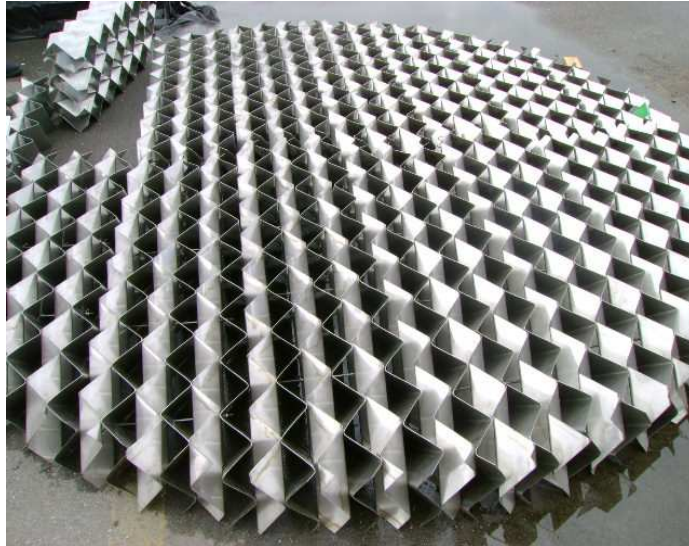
Paquete o elemento de empaque estructurado tipo Mellagrid.
